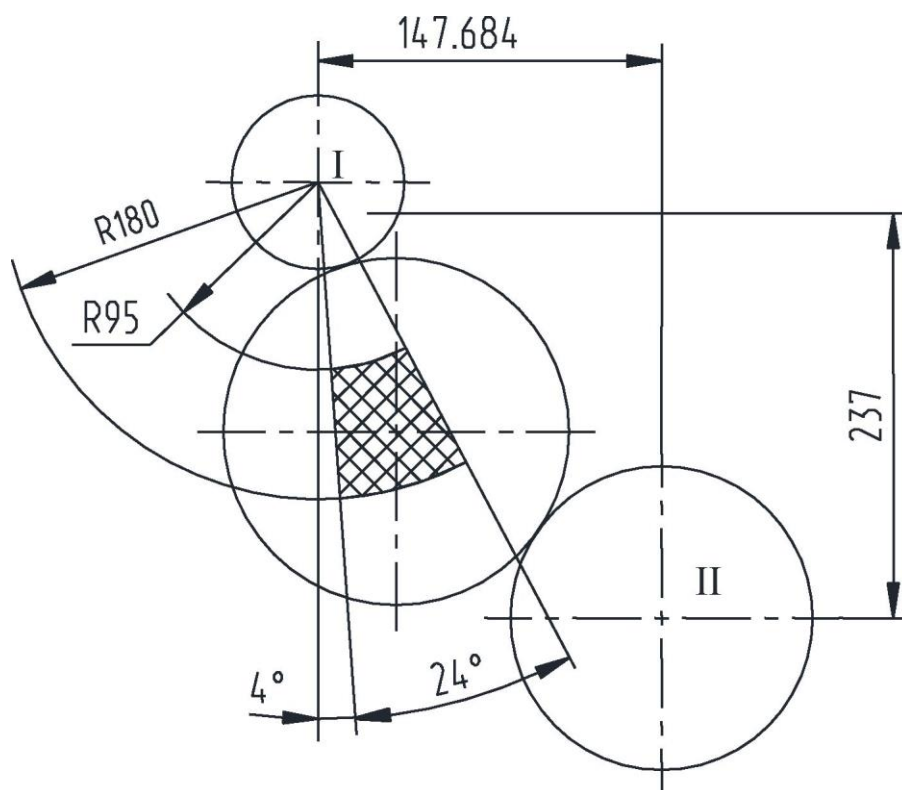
Чертеж для проверки возможности сцепления сменных зубчатых колес
